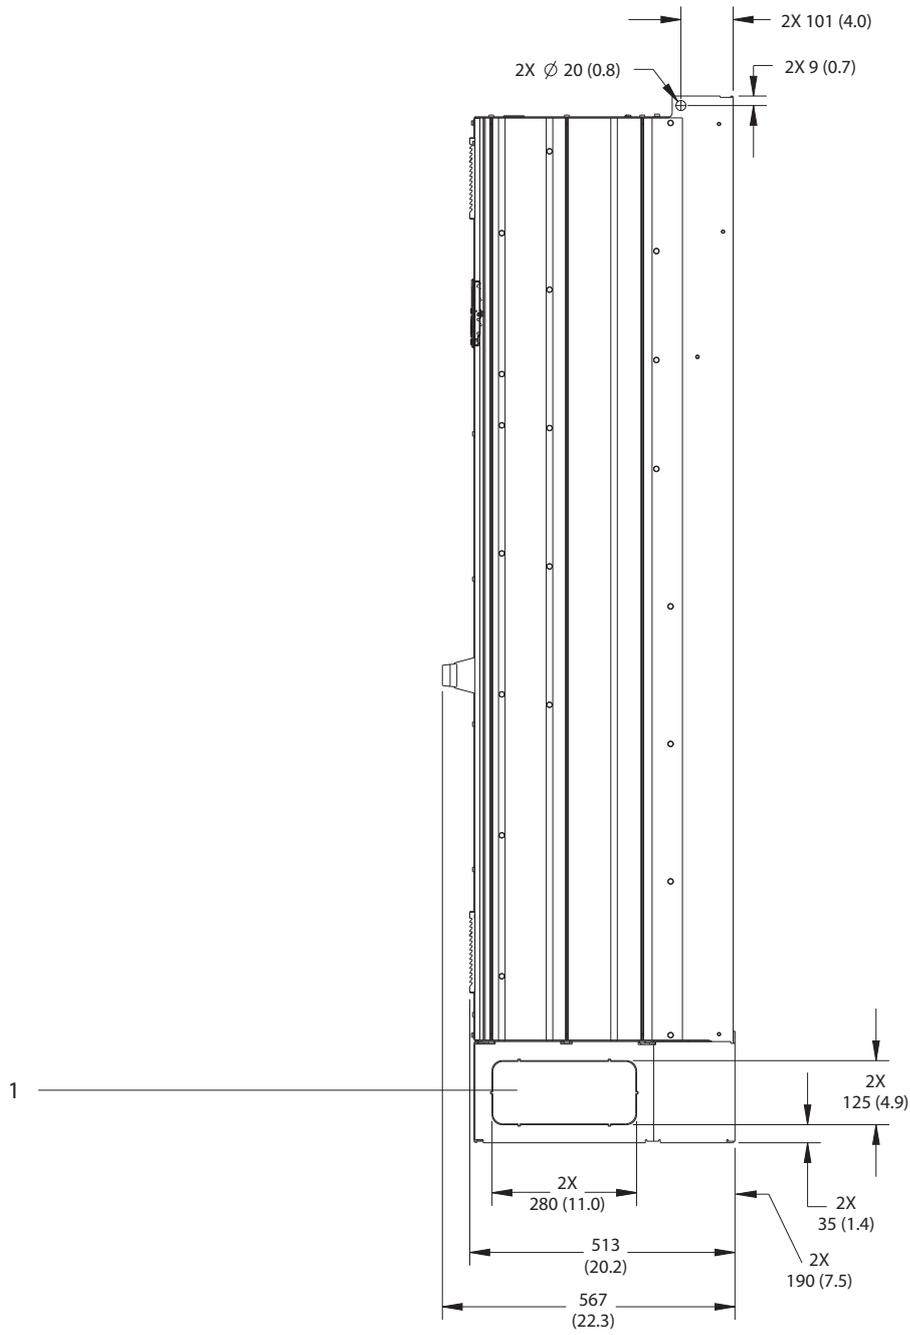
Espace pour la porte et dimensions de la plaque presse-étoupe du boîtier E1h
